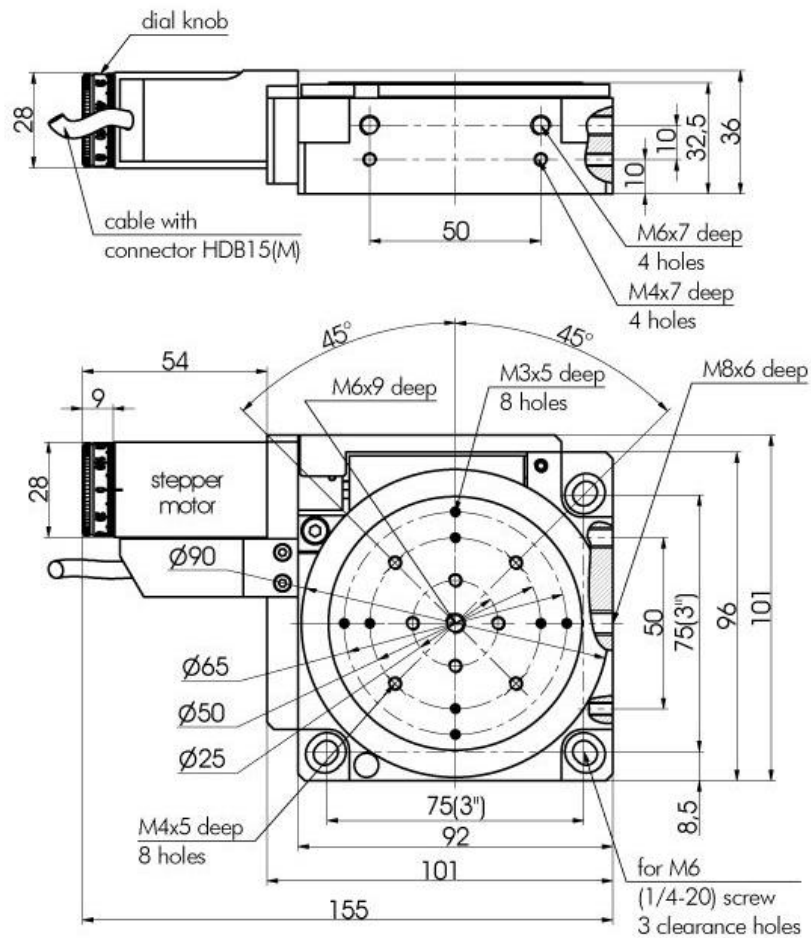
Чертёж габаритных размеров поворотного стола «Standa»
